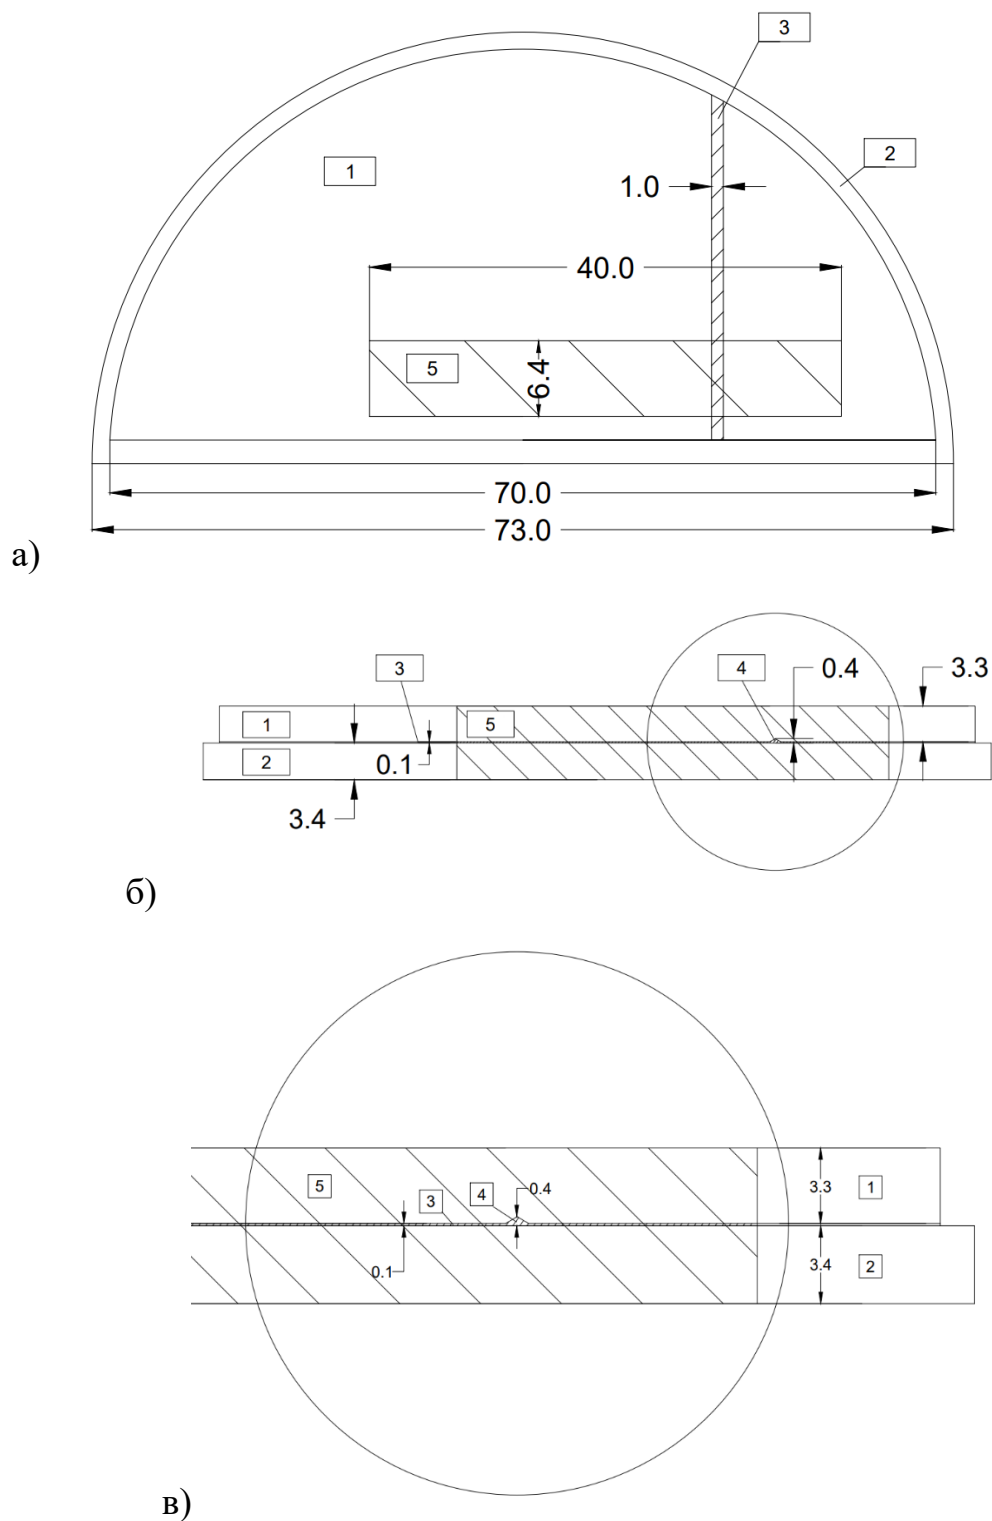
Схема образца АсА: а - вид сверху; б – вид сбоку;
